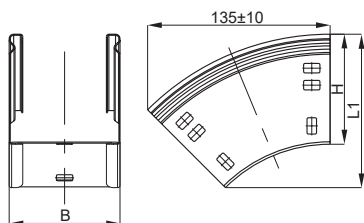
Поворот плавный на 45° вертикальный внешний / Figure B.2 – 45° vertical external smooth bend
